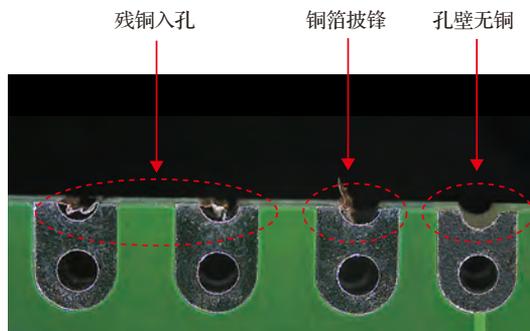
不按半孔工艺生产 PCB 的半孔案例图
